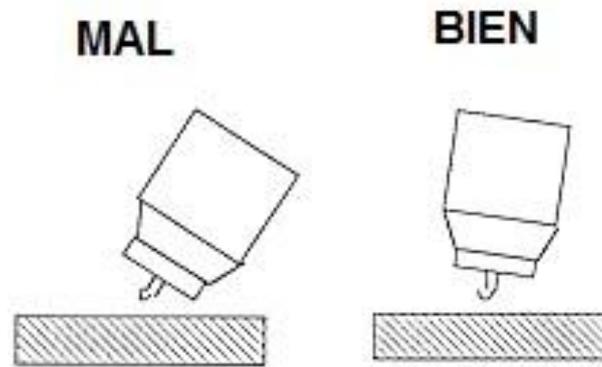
Corrección de la postura de soldadura TIG. [23]
